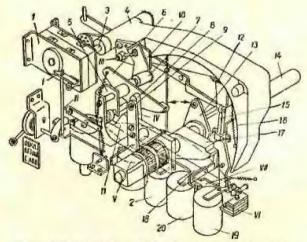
Кинематическая схема пружиниого привода типа ППМ -10.
